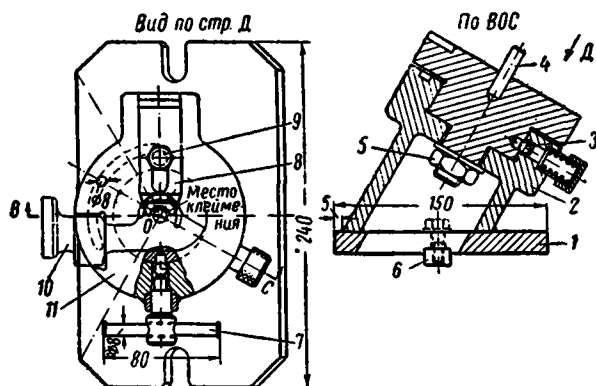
Приспособление для фрезерования шлицев в корпусе щеткодержателя двигателя ДК-403Г:
